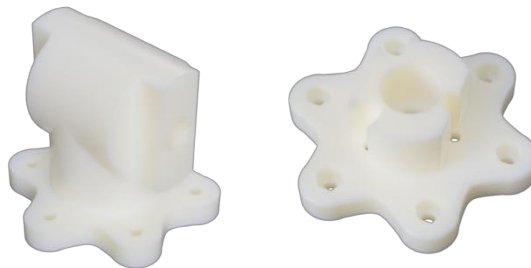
Renderizado 3D de las piezas de unión de la horquilla al motor
